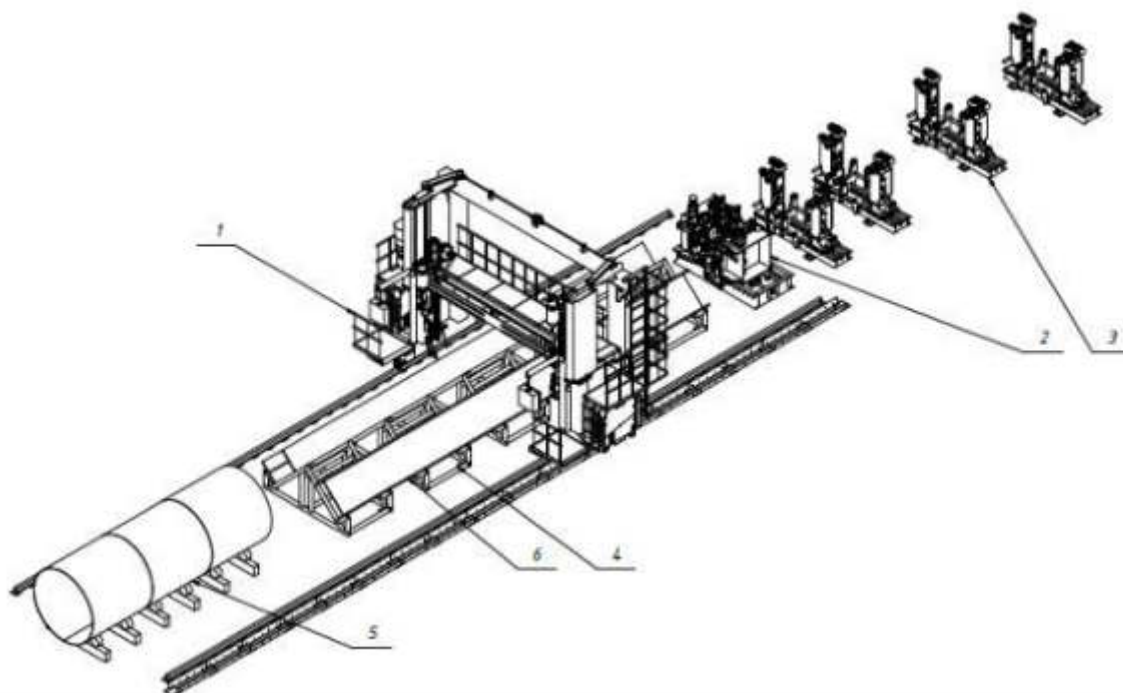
Принцип работы сварочного центра портального типа
